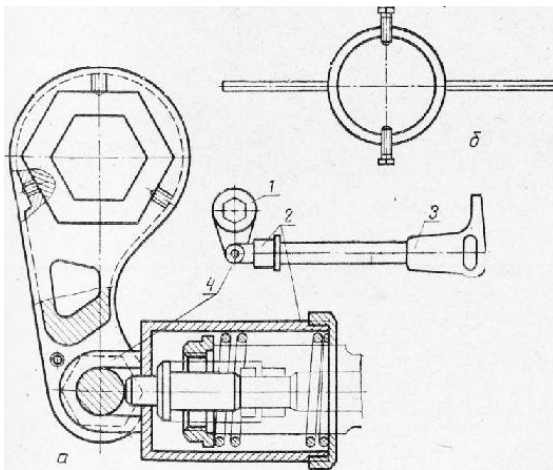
Ключи для отвертывания крупных гаек: а — пневматический для шестигранных: 1 — насадка; 2 — корпус насадки; 3 — пневматический клепальный молоток; 4 — шарнир; б — кольцевой для круглых шлицованных
